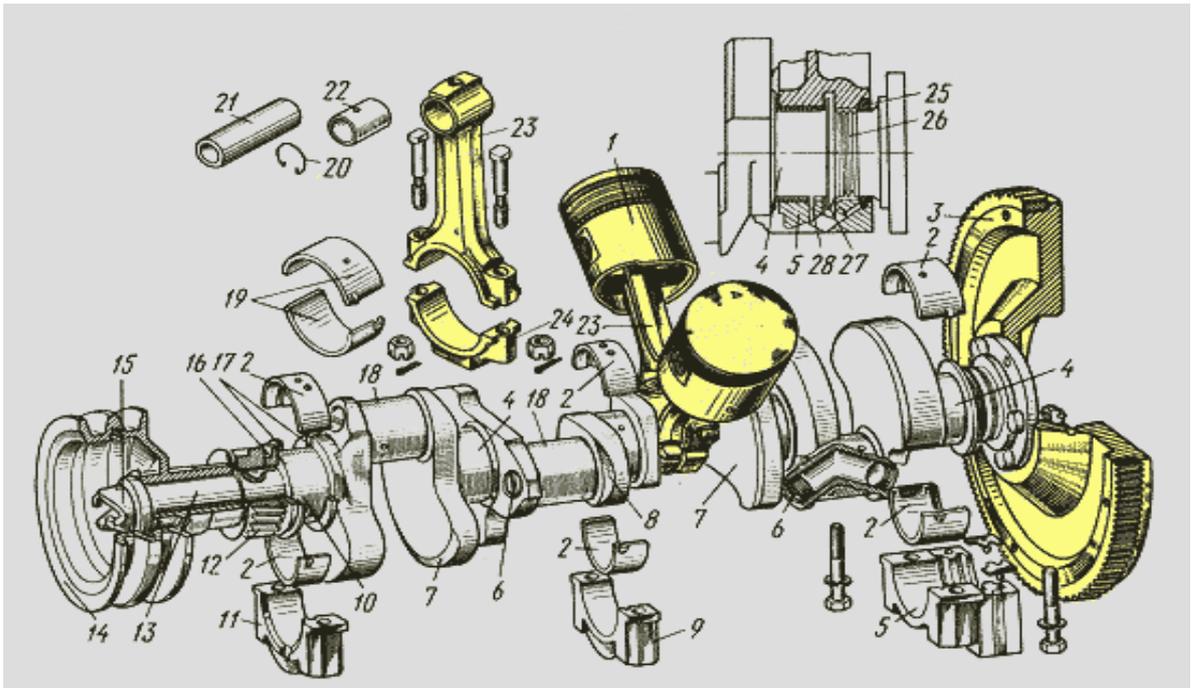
Деталі кривошипно-шатуного механізму двигуна:
